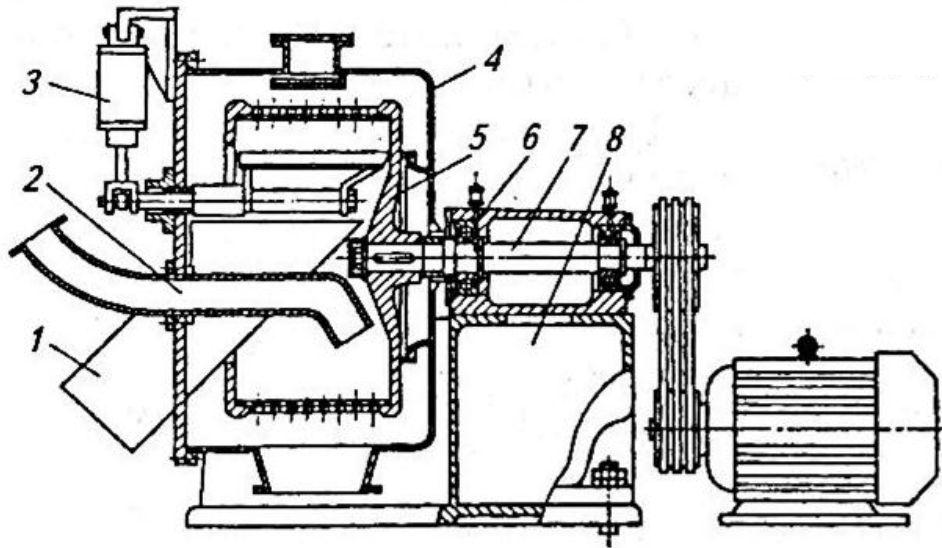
Схема центрифуги типа ФГН: 1 – разгрузочный бункер; 2 – питающая труба; 3 – механизм среза осадка; 4 – кожух; 5 – барабан; 6 – сальниковое уплотнение; 7 – приводной вал; 8 – станина
